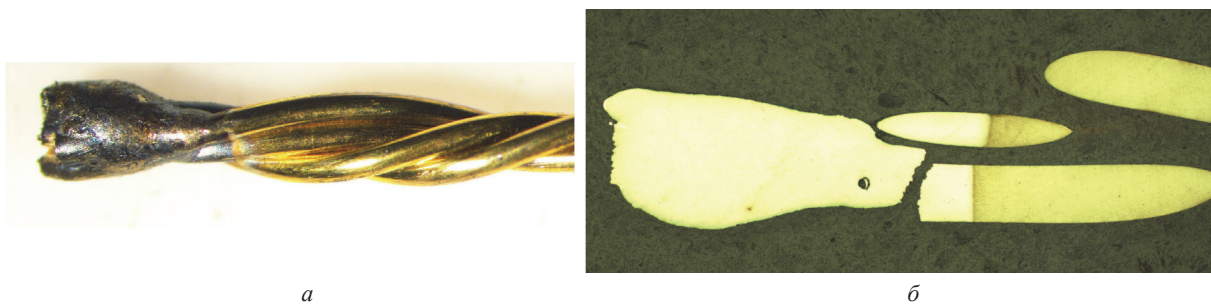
Сварка, выполненная без отпуска на металлокорде конструкции 2+2×0,32НТ: *а* – внешний вид разрушения после испытаний на разрыв. ×10; *б* – мартенсит закалки в микроструктуре сварного шва. ×100
